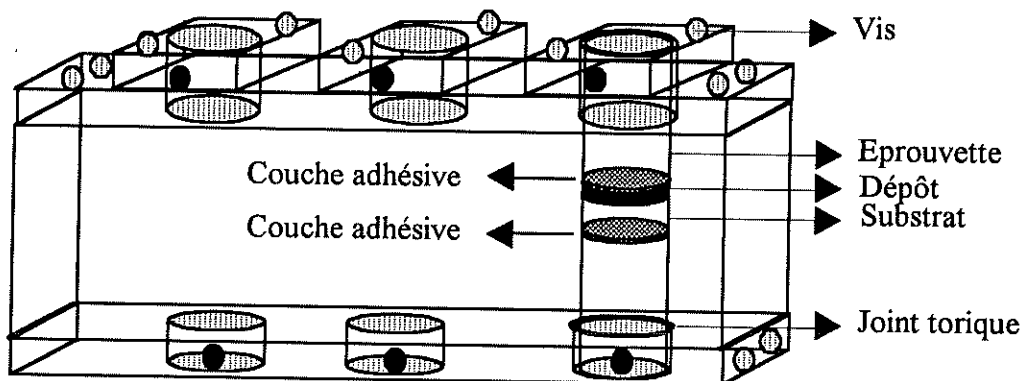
Dispositif pour l'assemblage des échantillons-éprouvettes destinés aux essais de traction.
